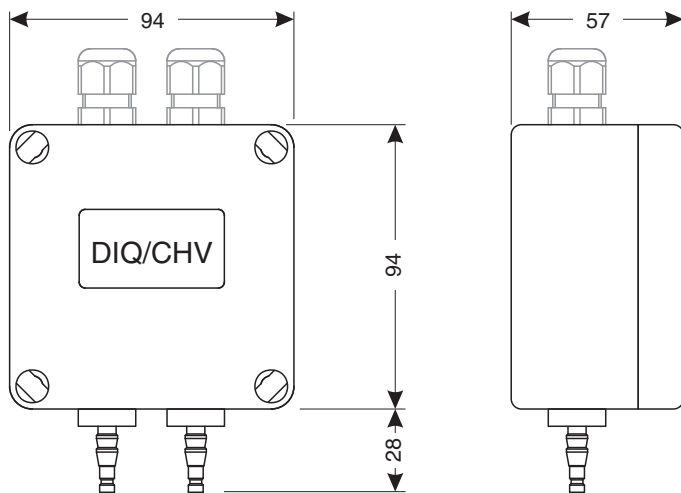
Maßzeichnung DIQ/CHV (Maße in mm)
